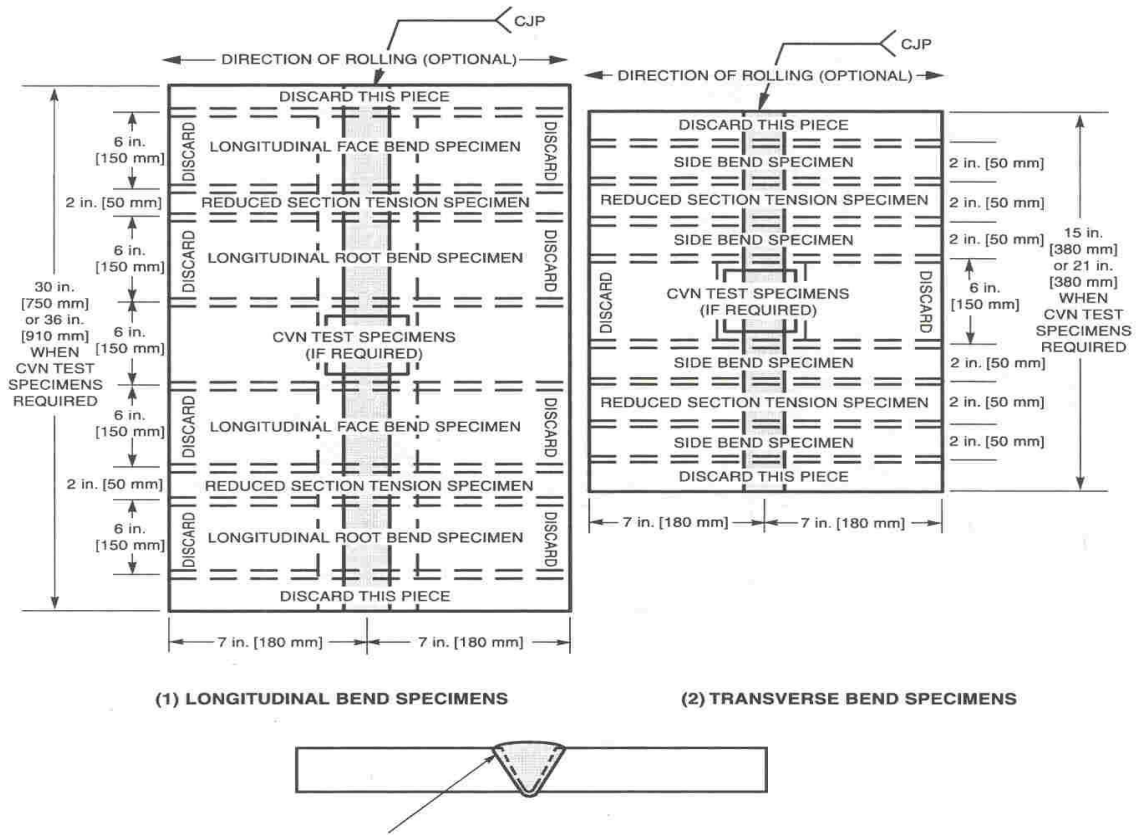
Especificación W.P.S para soldadura de bisel
